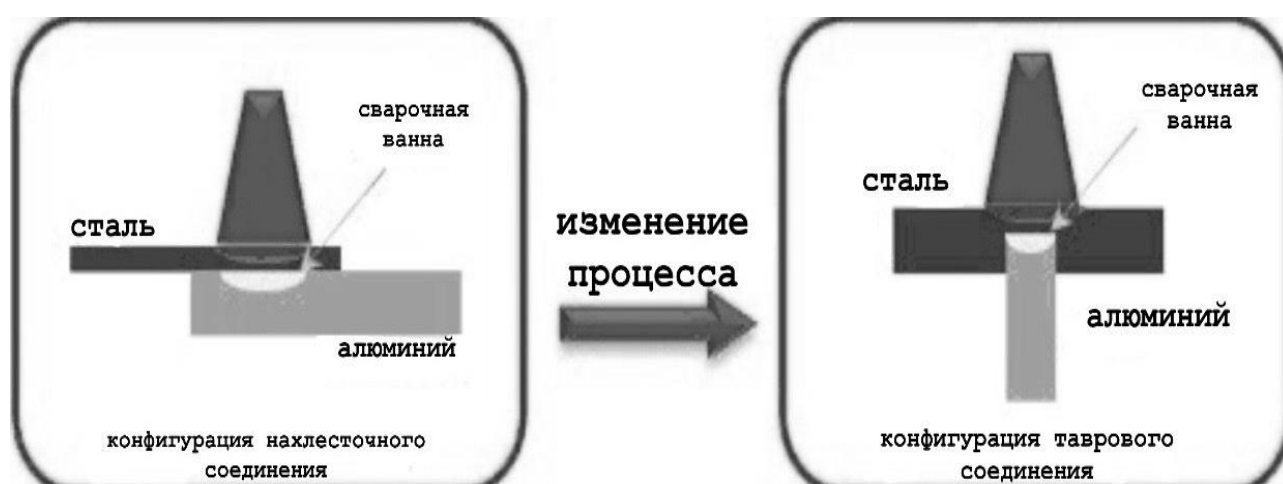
Схематичное изображение лазерной сварки стали с алюминием при переходе от нахлесточного соединения к конфигурации Т-образного соединения
